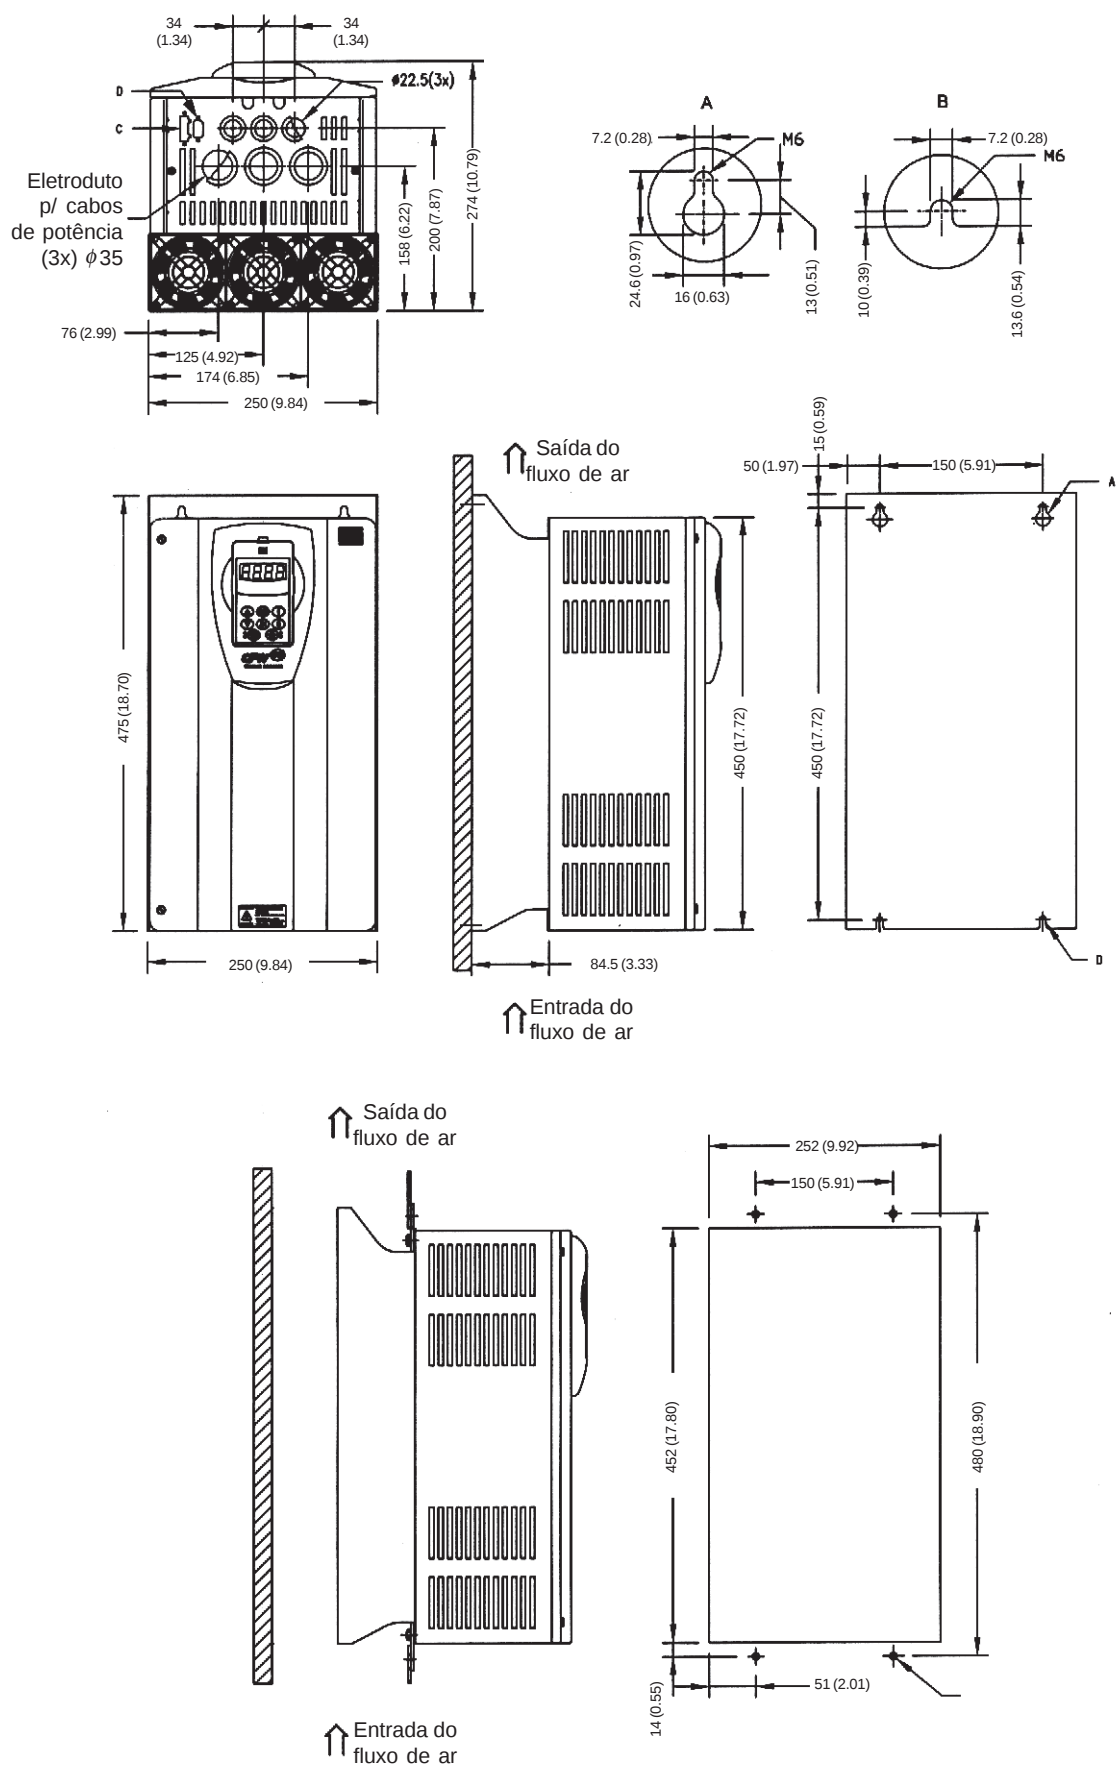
Mecânica 4 - Dimensões em mm (polegadas)
